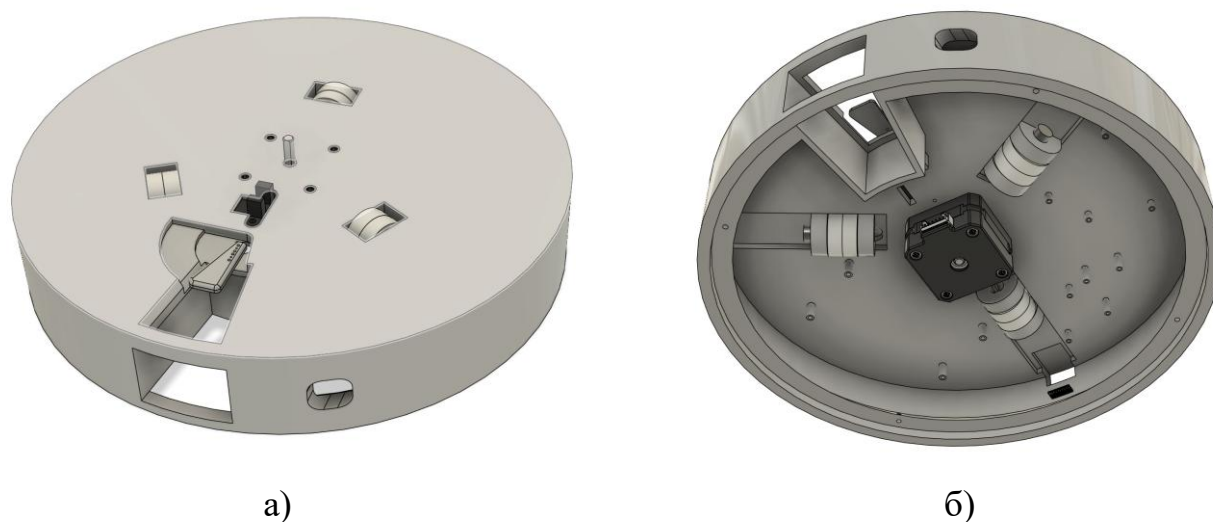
Основа конструкції диспенсеру: а – вид зверху; б – вид знизу
